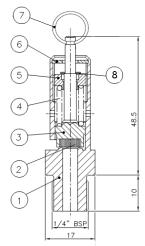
Клапан предохранительные типа RA 81806: 1 – корпус; 2 – уплотнение; 3 – шток; 4 – пружина; 5 - регулятор; 6 - проволока и пломба; 7 – подъемное устройство; 8 - кольцо стопорное; 9 – выход организованного дренажа.
